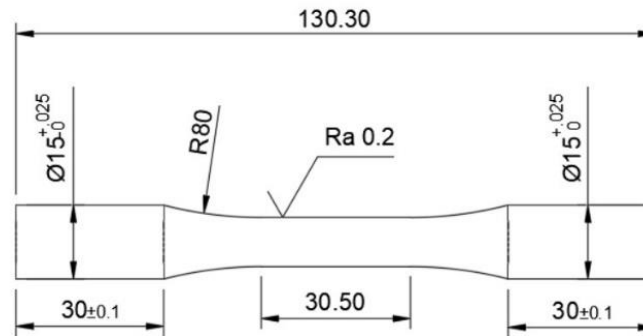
Corpo de prova cilíndrico dimensionado de acordo com a norma ASTM E-466 para ensaios de fadiga
